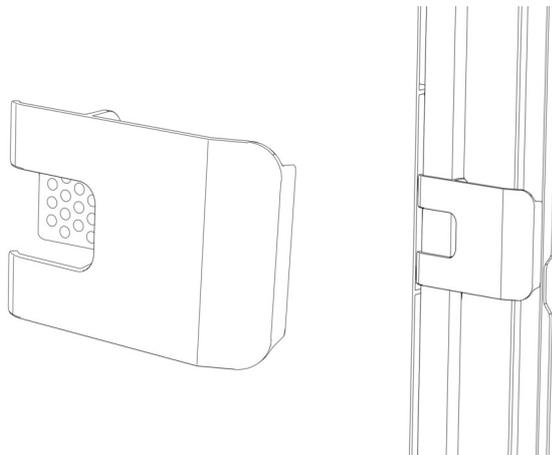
Schlauchklammer (links); Schlauchklammer installiert (rechts)
